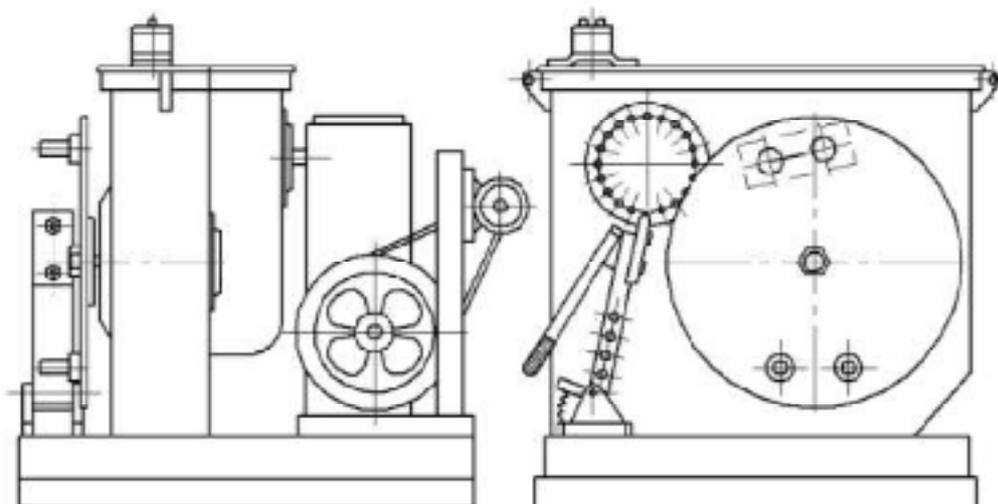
Станок для снятия тормозных грузовых автомобилей с вертикальным расположением поворотной плиты и срезывающего устройства
